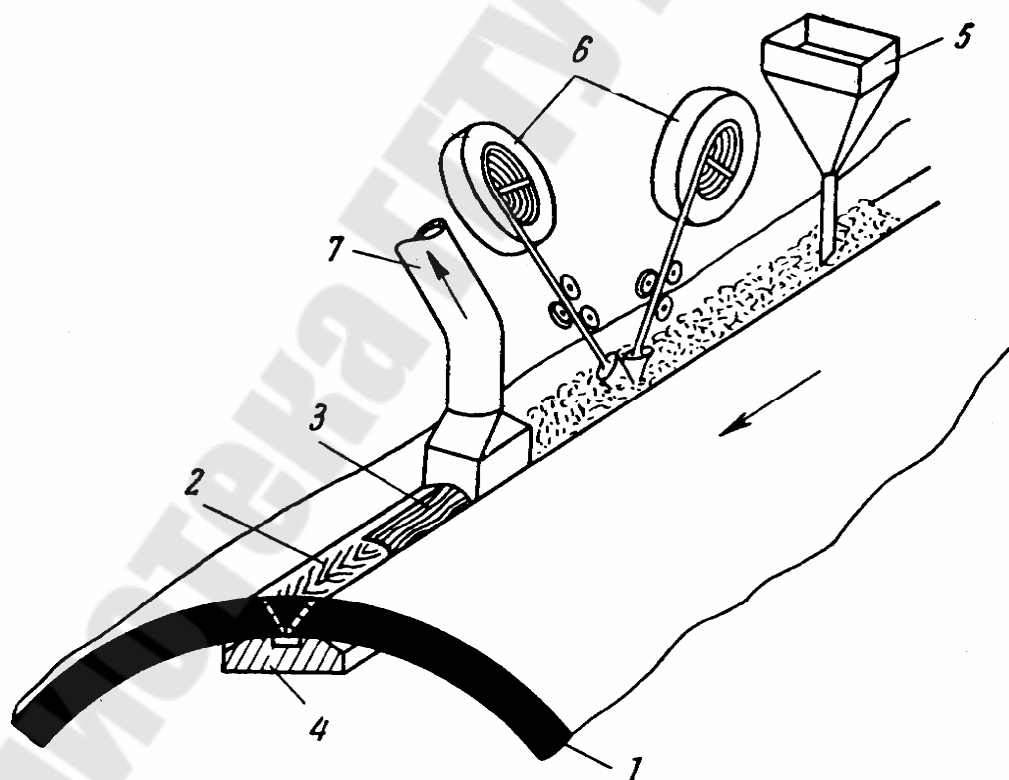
Схема сварки труб под слоем флюса:
